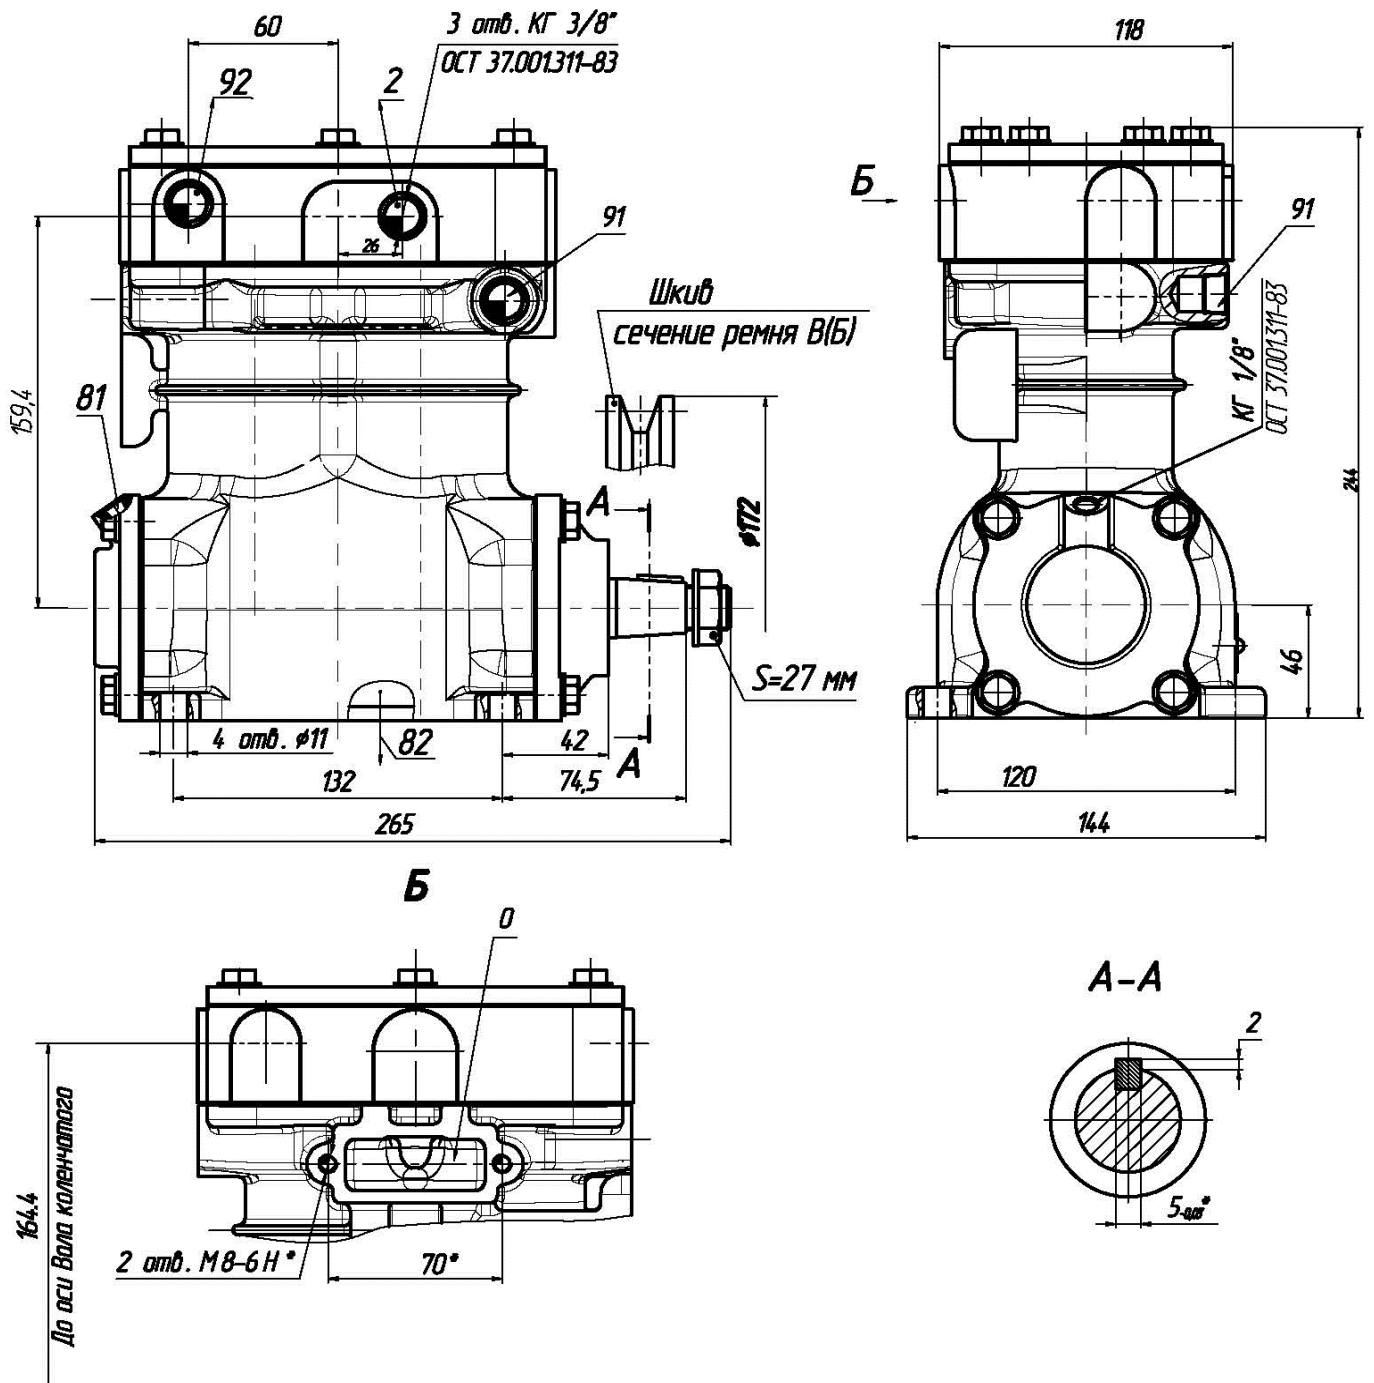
Присоединительные и установочные размеры компрессора АМ.3509012-161. Маркировка отверстий: 0 — всасывание; 2 — нагнетание; 81 — подвод масла; 82 — слив масла; 91 — подвод охлаждающей жидкости; 92 — отвод охлаждающей жидкости.
